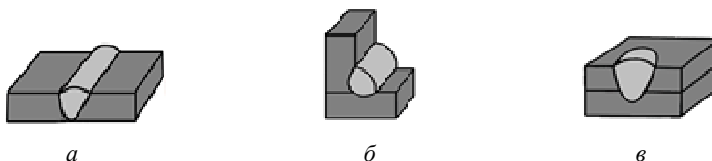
Классификация сварных швов по форме поперечного сечения:
